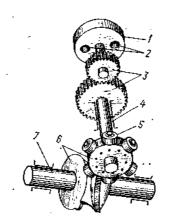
Схема привода матричного блока двухударного двухпозиционного автомата
